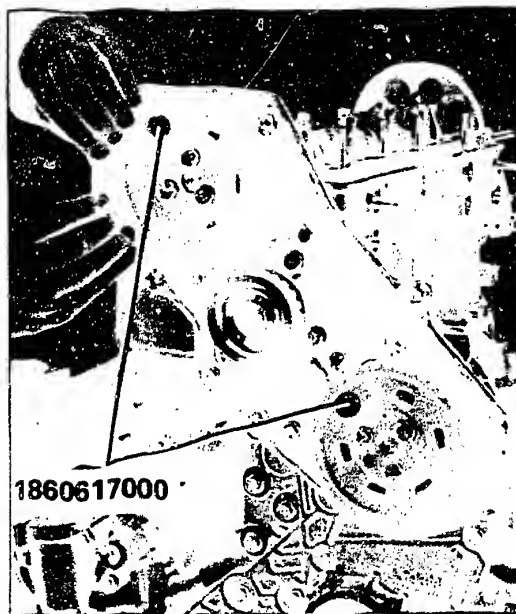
Motor 2500 turbo ds: Auflegen des Zahnriemens am Einspritzpumpenrad und am Steuerrad der Nockenwelle, die beide mit dem Dorn in der korrekten Position zu arretieren sind. Dieselbe Grundeinstellung ist am Einspritzpumpenrad beim Einbau der Einspritzpumpe vorzunehmen.
